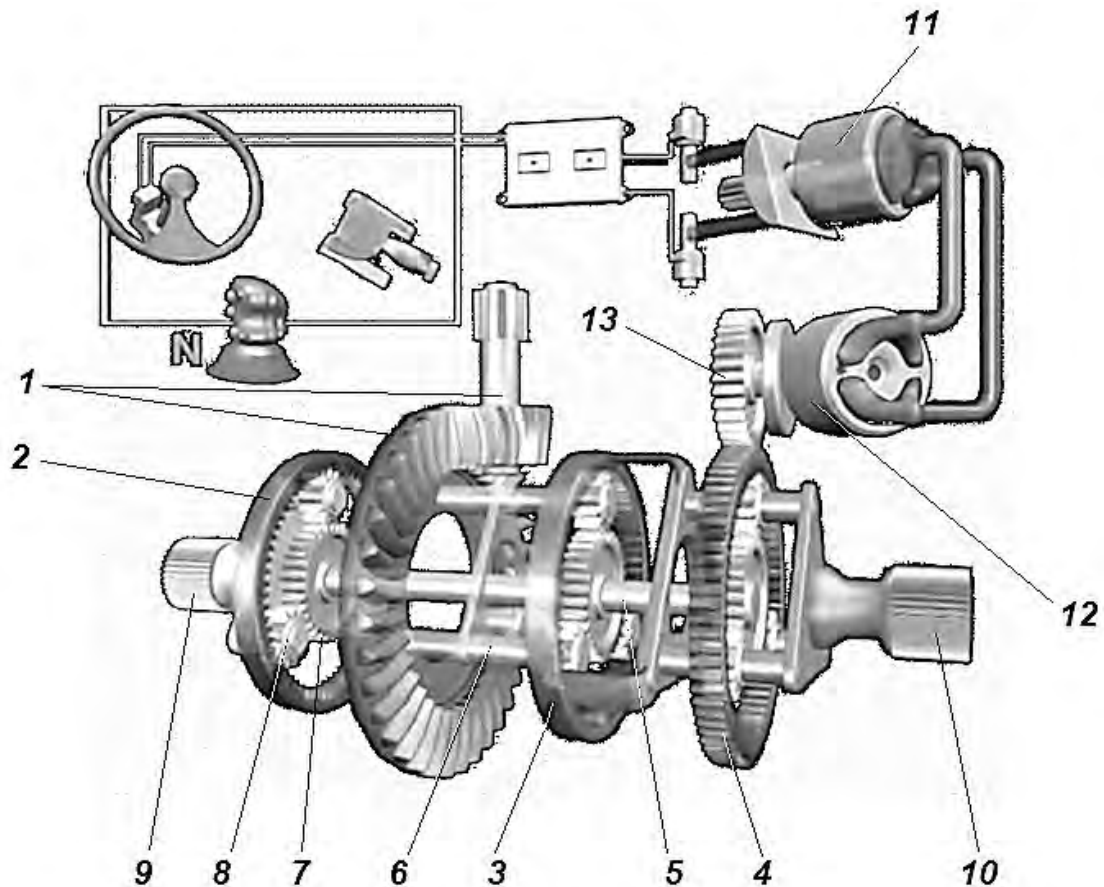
Безступінчастий механізм повороту трактора типу
